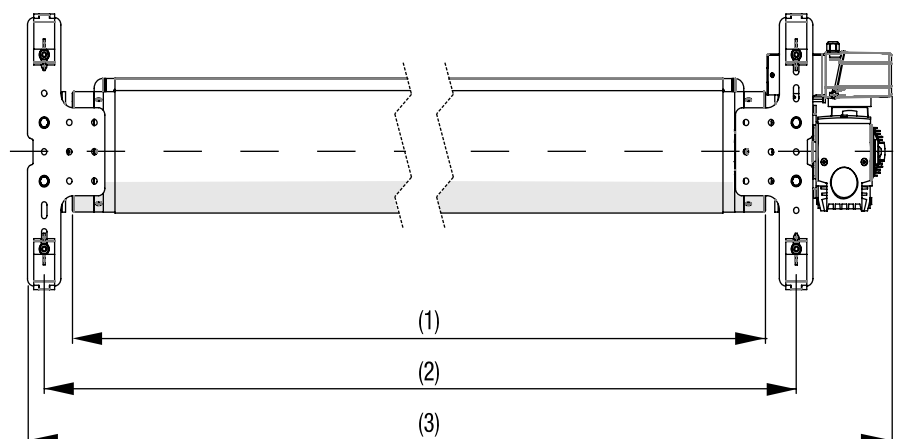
Rollbildwand TUBE – Maße Draufsicht
